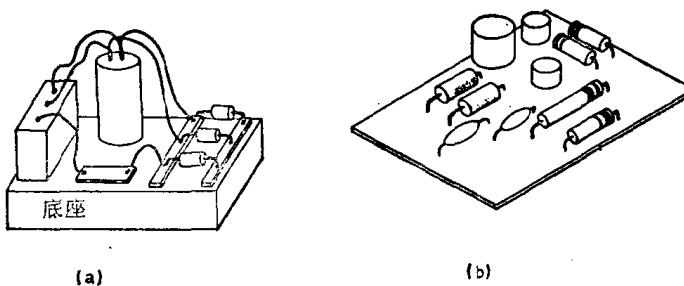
使用分立元件的早期电子设备装配板：(a) 焊点到焊点的连接；(b)pcb (印刷电路板) 或称pwb (印刷布线板)
